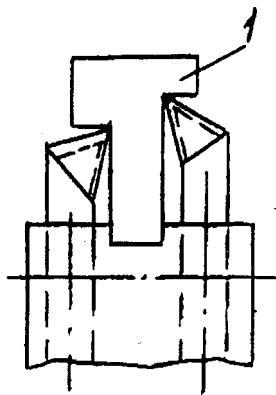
Шаблон для настройки резцов на токарном станке
